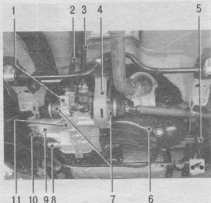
Расположение коробки передач на автомобиле (вид снизу): 1 – коробка передач; 2 – тяга привода управления коробкой передач; 3 – реактивная тяга привода управления коробкой передач; 4 – задняя опора силового агрегата; 5 – правая опора силового агрегата; 6 – двигатель; 7 – внутренние ШРУСы; 8 – соленоид блокировки включения передачи заднего хода; 9 – выключатель света заднего хода (на фото не виден); 10 – левая опора силового агрегата; 11 – пробка отверстия для слива масла
